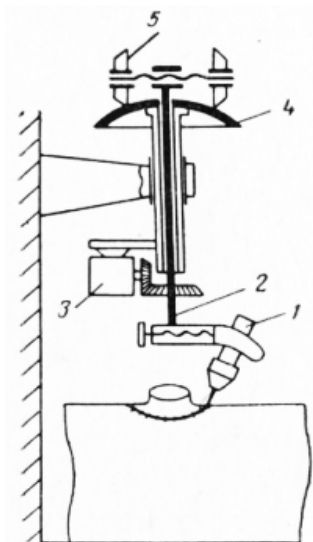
Схема установки для обварки штуцеров по копиру:
